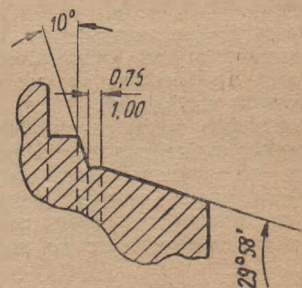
Профиль конуса червяка, полученный обточкой на токарном станке.
